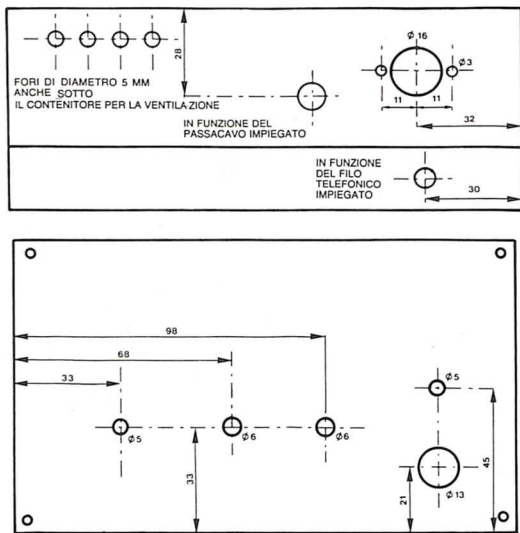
Il dispositivo è stato inserito in un contenitore a leggio TEKO, il cui frontale deve essere forato come indicato nel disegno.
